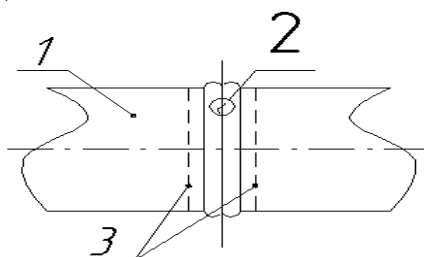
Удаление дефекта: 1 – трубная конструкция; 2 – дефект в сварном шве; 3 – линия отреза (с
